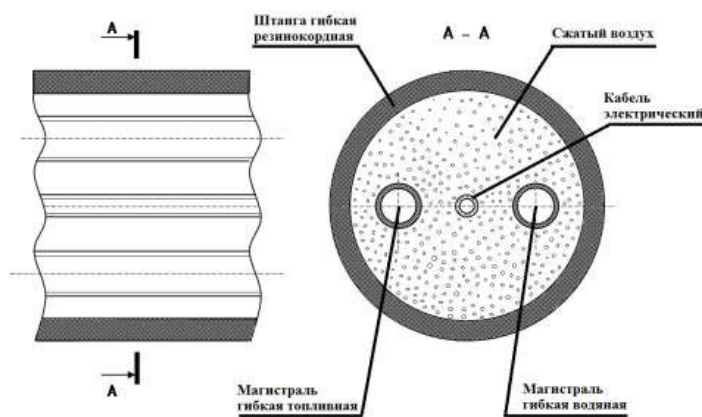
Схема сечения резинокордной гибкой штанги
